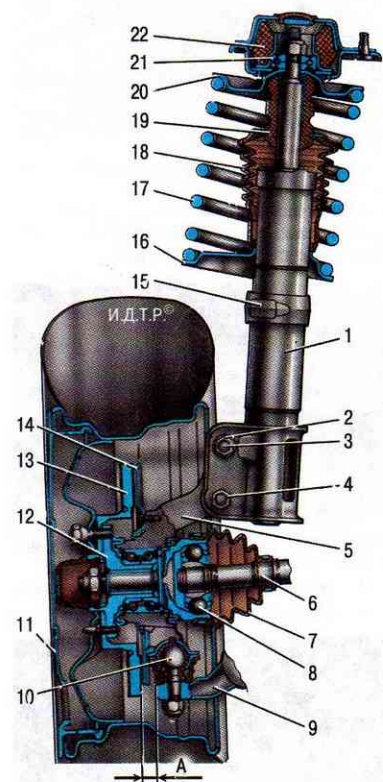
Передняя подвеска в сборе: 1 – телескопическая стойка; 2 – гайка; 3 – эксцентриковый болт; 4 – гайка; 5 – поворотный кулак; 6 – вал привода переднего колеса; 7 – защитный чехол шарнира; 8 – наружный шарнир вала; 9 – нижний рычаг; 10 – шаровая опора; 11 – декоративный диск (коллап) колеса; 12 – ступица; 13 – тормозной диск; 14 – защитный кожух; 15 – поворотный рычаг; 16 – нижняя опорная чашка; 17 – пружина подвески; 18 – защитный чехол телескопической стойки; 19 – буфер хода сжатия; 20 – верхняя опорная чашка; 21 – подшипник верхней опоры; 22 – верхняя опора стойки; А – контрольный размер
